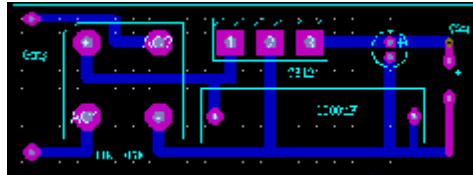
PCB şemanın Y ekseninde 180° döndürülmüş hali
